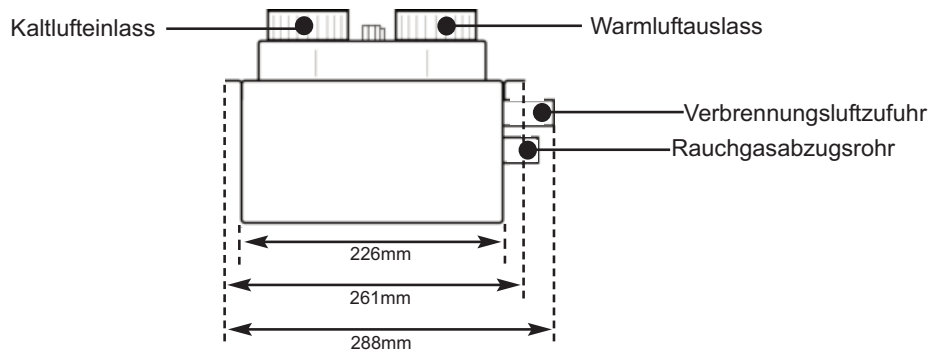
Unterbodenmontage - Frontansicht - SH2211 oder SC2211
